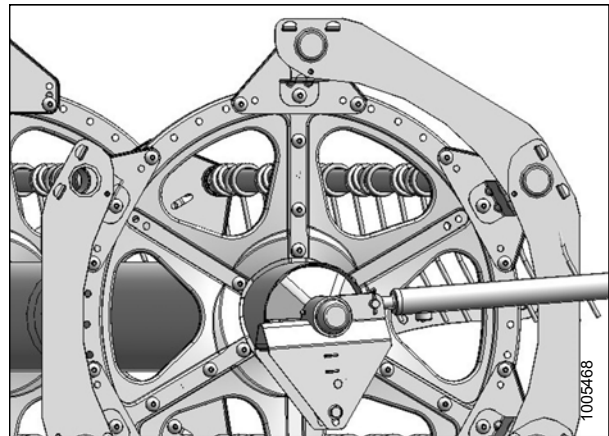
Ausgebautes Haspel-Seitenblech
